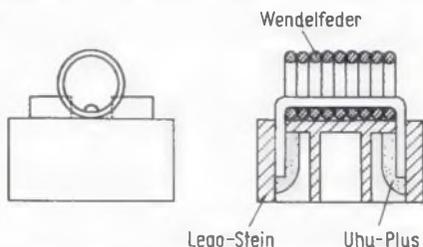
Aufbau eines Bausteines mit Feder zum Befestigen von Drähten
